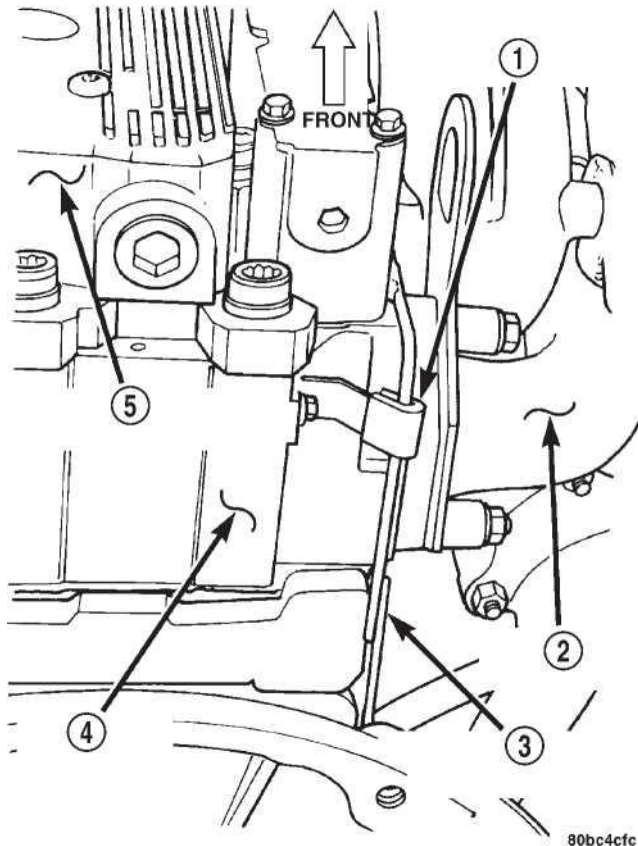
Стопорный зажим линии подачи масла головки цилиндра
